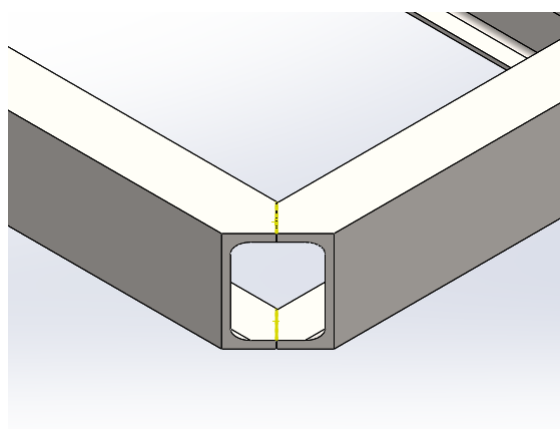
Detalle de soldadura de esquina delantera
